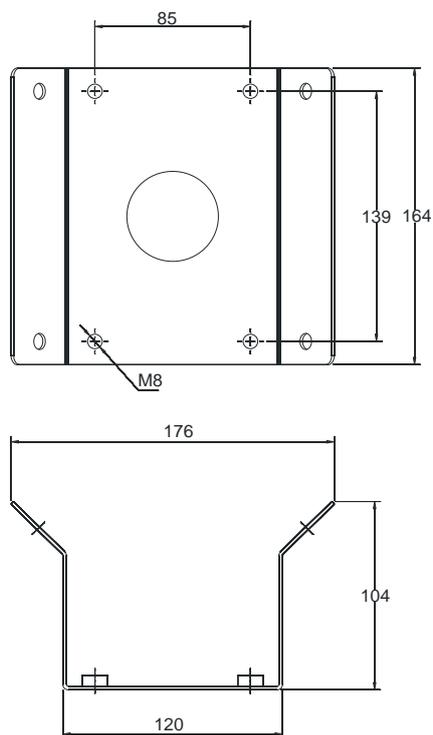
Bild mit den Abmessungen der an der Außenwand montierten Installationshalterung
